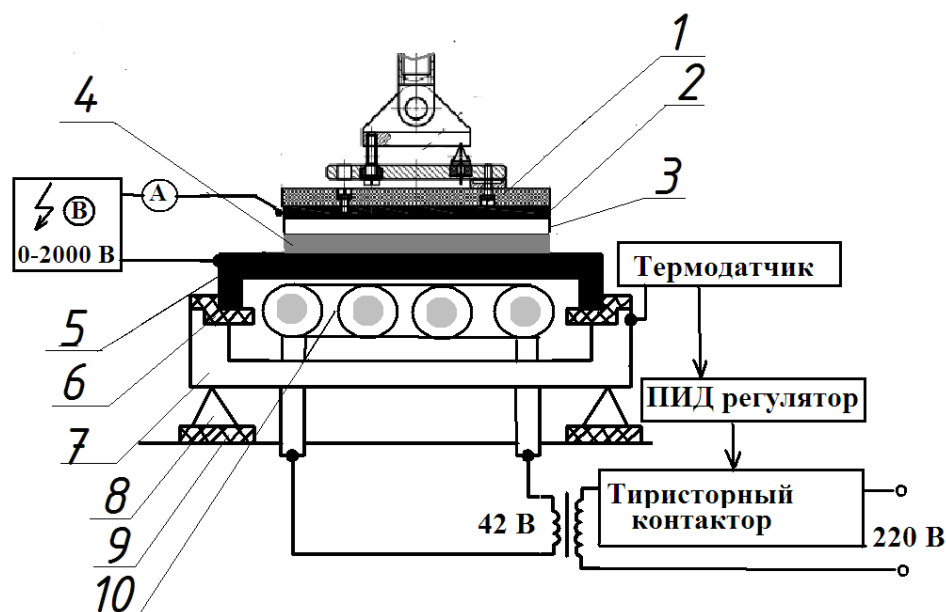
Принципиальная схема установки анодной сварки:
